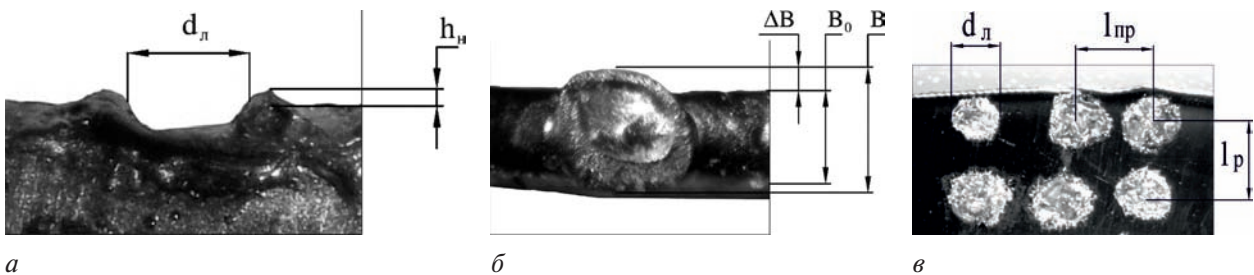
Фотография единичной лунки на наружной поверхности диска: а — вид сбоку; б — вид в плане (увеличение 150°); в — фотография лунок на боковой поверхности диска (увеличение 30°)
